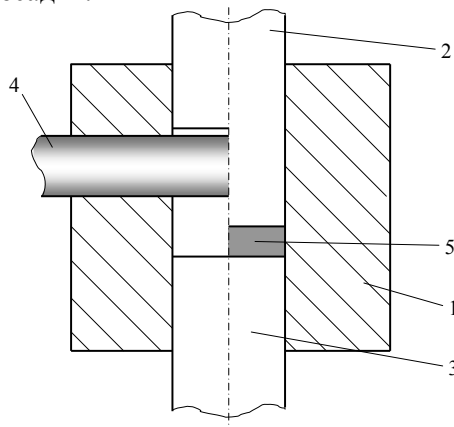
Принципова схема процесу відрізання-штампування для виготовлення циліндричних заготовок з алюмінієвого прутка: 1 - матриця, 2 - пуансон, 3 - виштовхувач, 5 - пруток, 8 - заготовка, що осаджується
